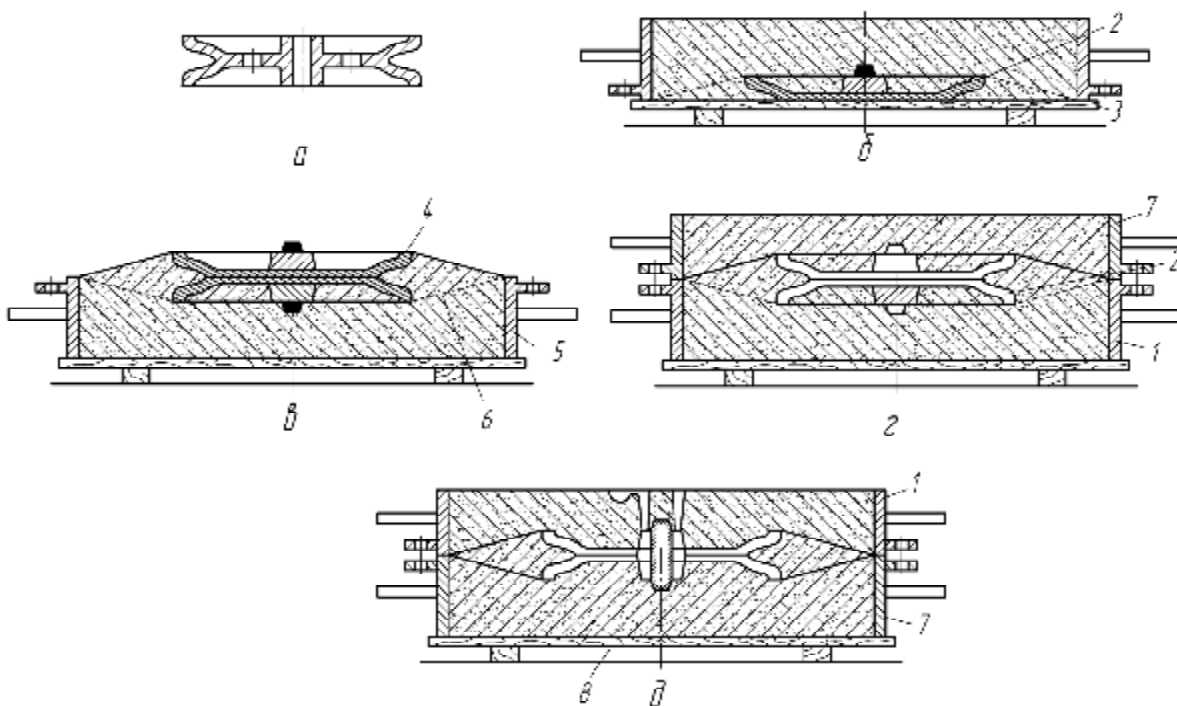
Схема формовки по модели с перекидным «болваном»:
